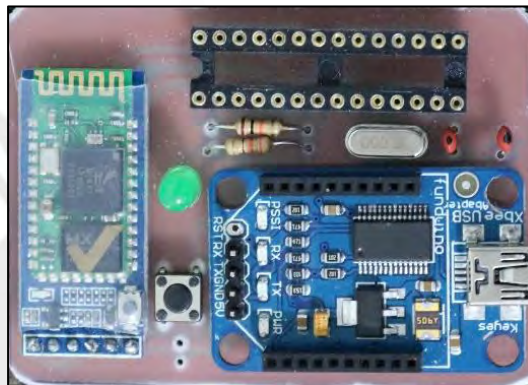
Imagen de los componentes sujetos por soldadura al circuito impreso.
